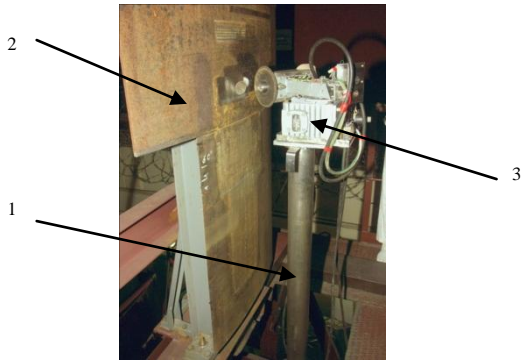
Розташування модуля шліфування на стенді ЮУ АЕС: 1 – телескопічна штанга маніпулятора; 2 – імітатор корпусу реактора; 3 – модуль шліфування
